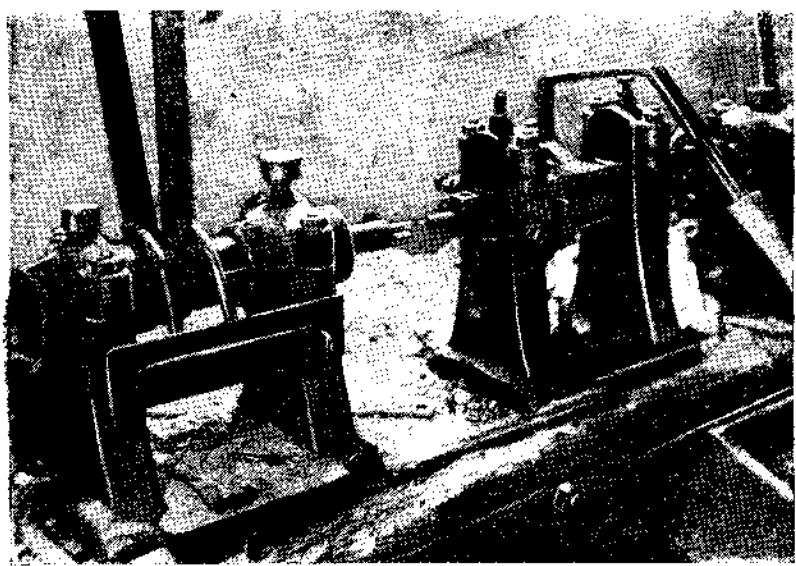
Общий вид станка с гребенчатой подачей (2-я рука).
